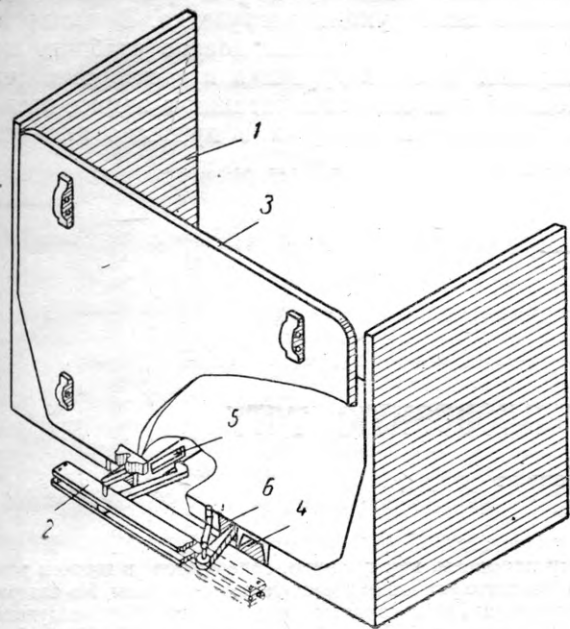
Конструктивная схема устройства для механизированной погрузки коротыя
